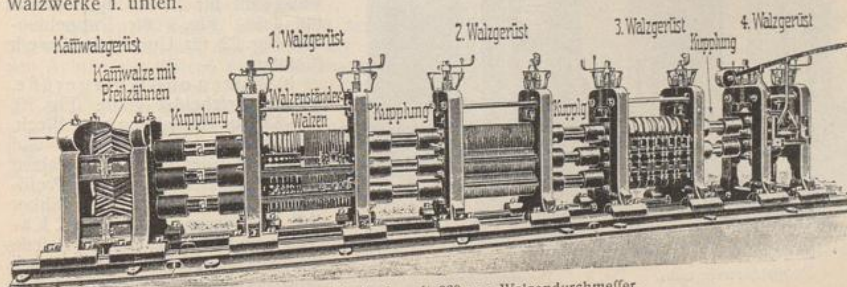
Feineisenstraße mit 260 mm Walzendurchmesser.
